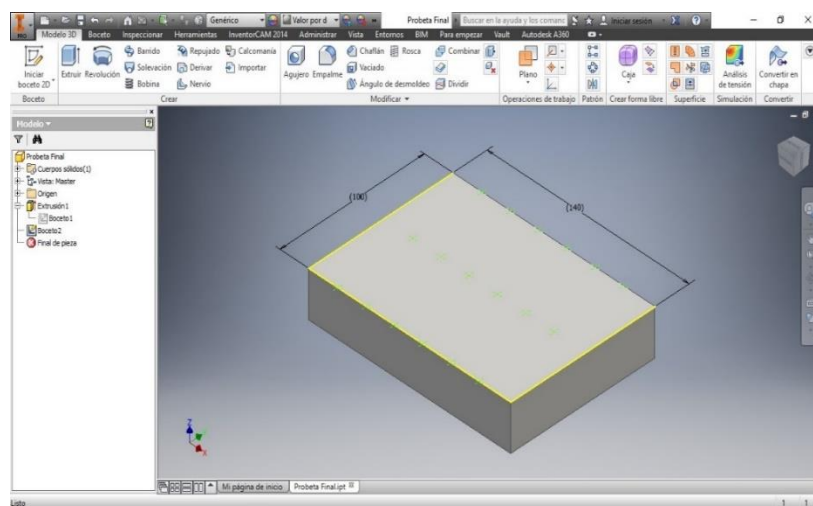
La placa base de aluminio Prodax con dimensiones nominales para el mecanizado de probetas.
